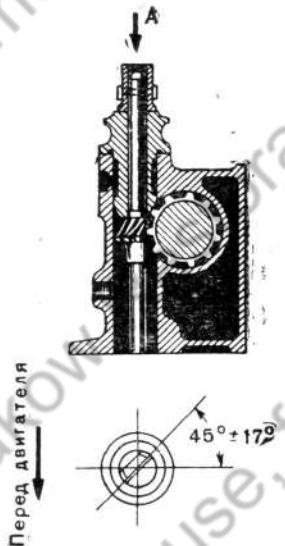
Положение валика масляного насоса для установки прерывателя-распределителя P-15
